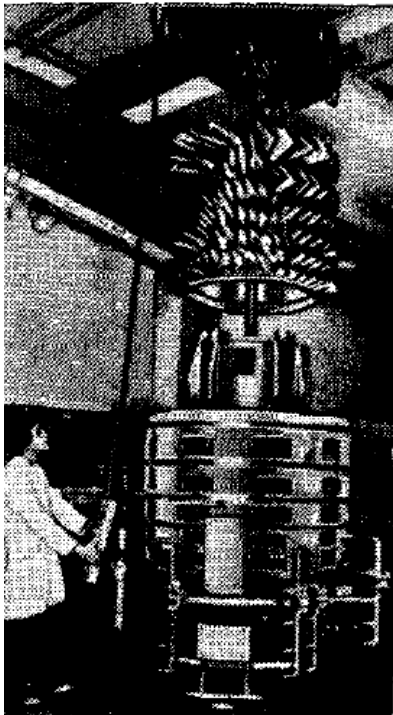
Установка ротора осевого компрессора (3500 кВт) в сборку корпуса статора
